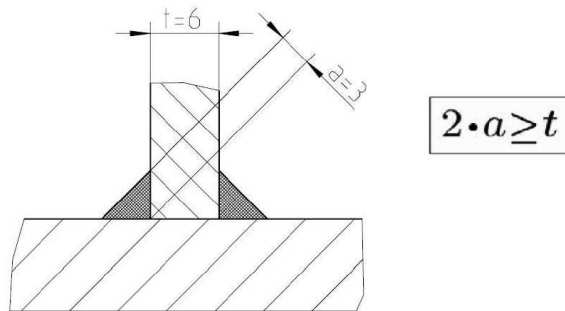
Blech mit Kehlnähten querschnittsdeckend gegengeschweißt
